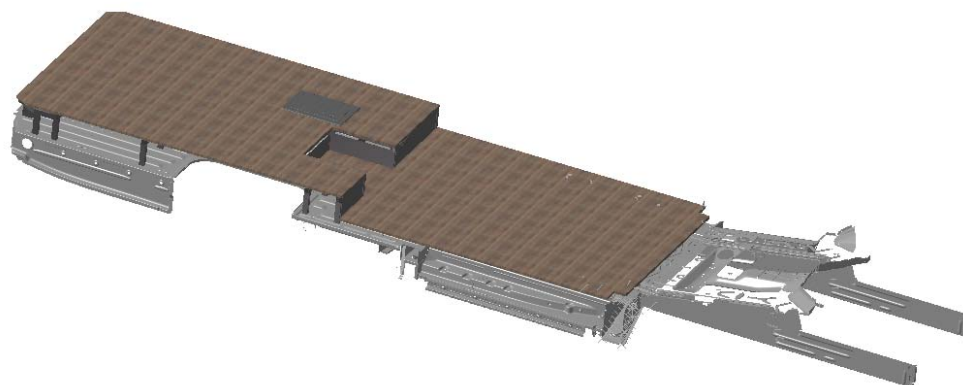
Colocación tapa calefacción sobre el vehículo.
